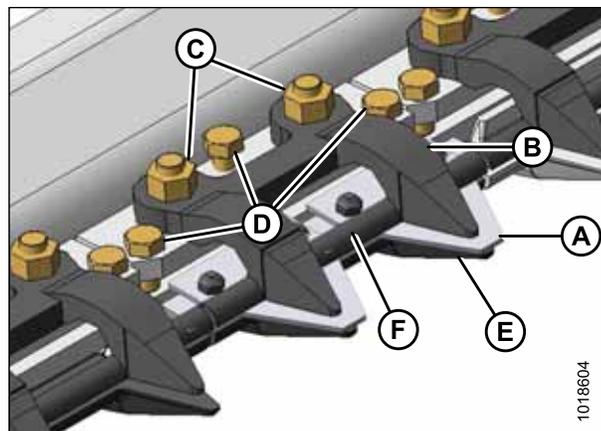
Стандартный кованный прижим укороченного противорежущего пальца
